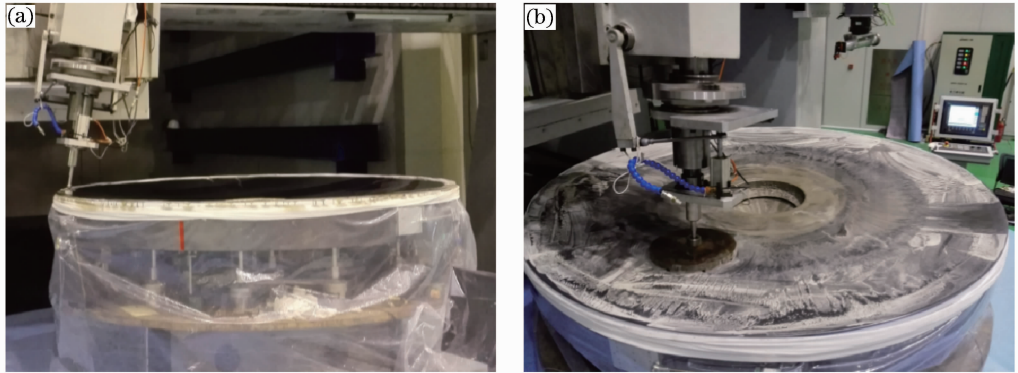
FSGJ-4500 加工 2040 mm 口径非球面碳化硅反射镜实物图。(a) 100 mm 磨头加工过程;
